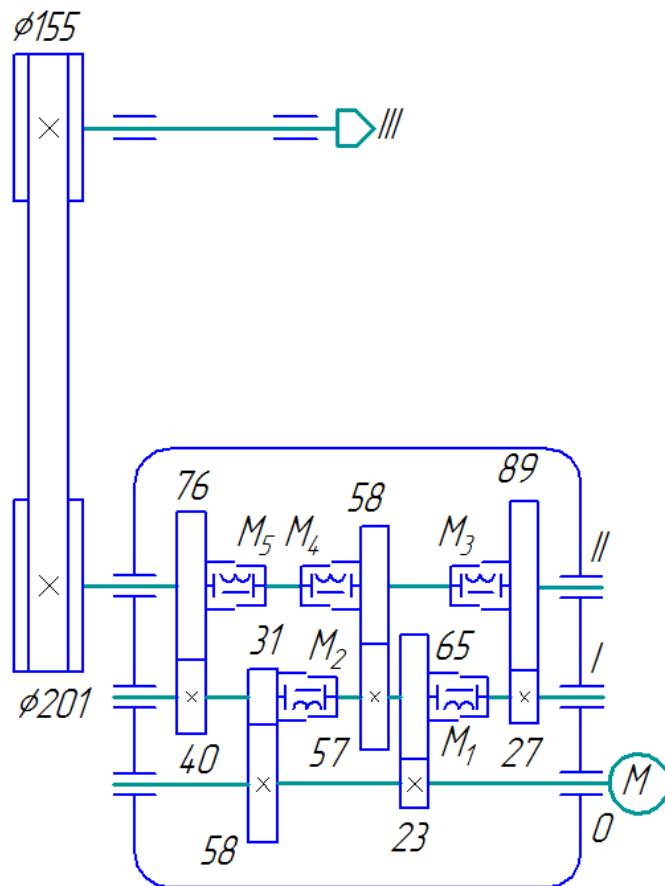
Кинематическая схема ПГД токарно-револьверного станка мод.1П326
